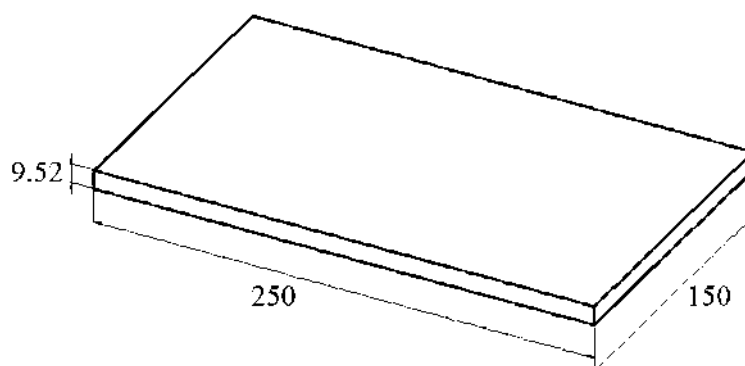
Dimensiones de la placas de metal base (cotas en mm).
